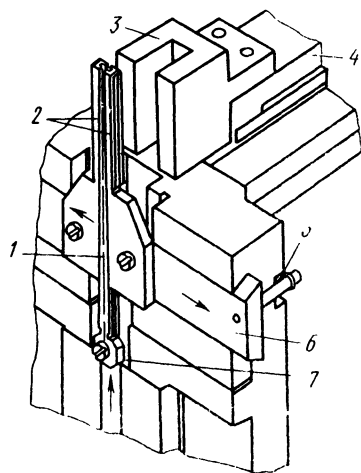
Приспособление для растяжки сеток и правки их траверс: 1 — клин, 2 — оправка, 3 — растягивающий шаблон, 4, 6, 7 — ползунки, 5 — пружина
